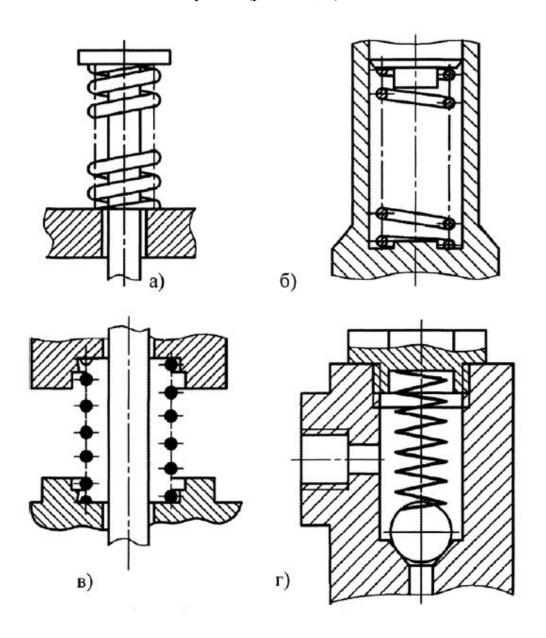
Способы изображения пружин на сборочных чертежах: а -на виде; б - в разрезе; в - в разрезе допускаемое; г - условное
